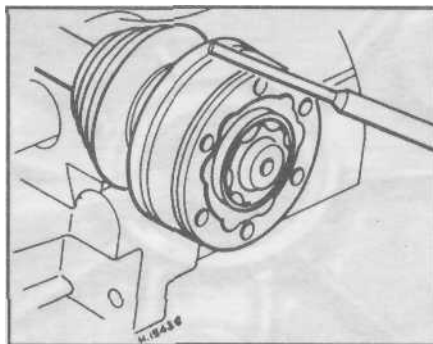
Снятие пластмассовой крышки с корпуса внутреннего шарнира
